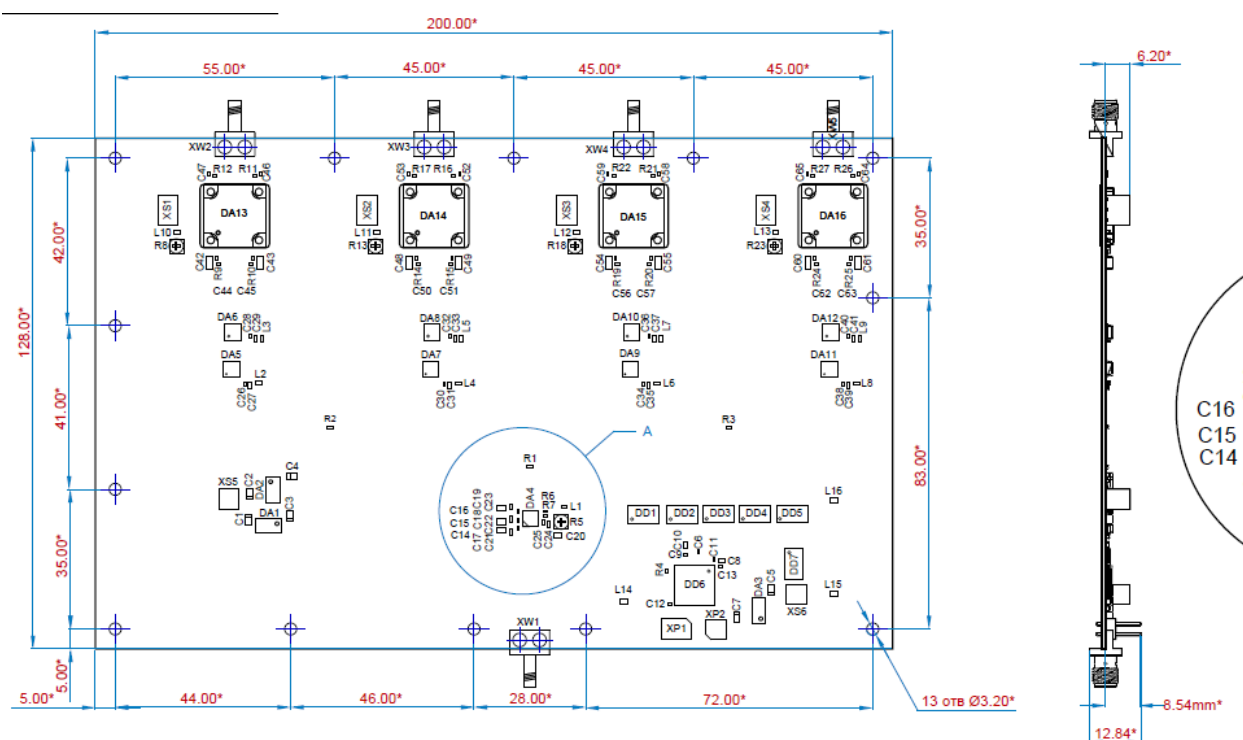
Фрагмент сборочного чертежа на печатный узел
